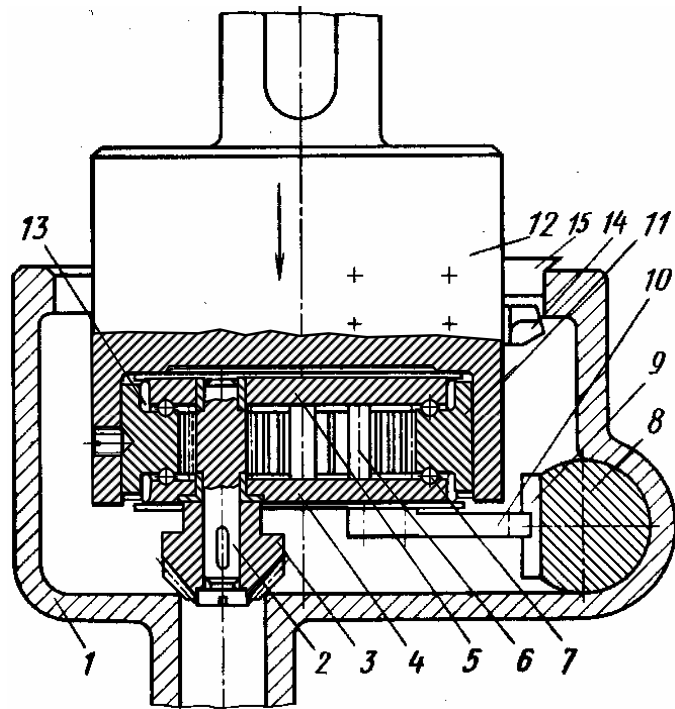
Інструментальна головка конструкції ЗІЛ для обробки отворів, розташованих на заданій відстані від осі обертання заготовки
